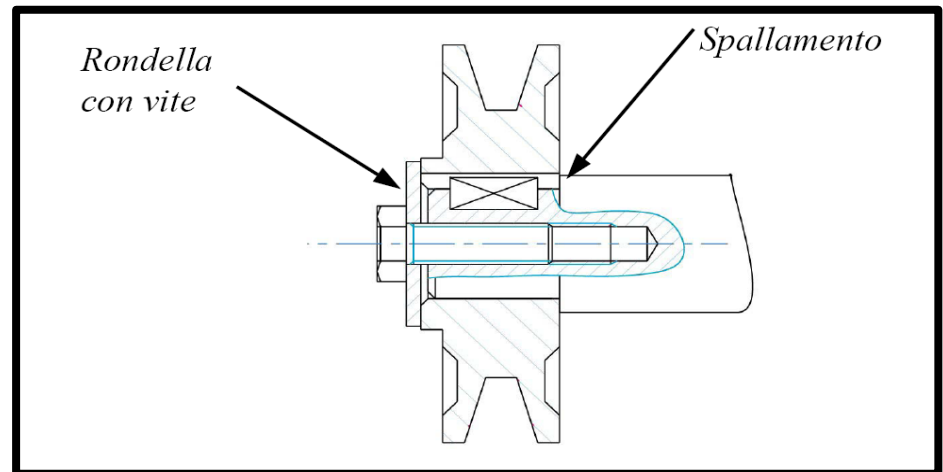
Esempio di bloccaggio assiale mediante spallamento e vite.
